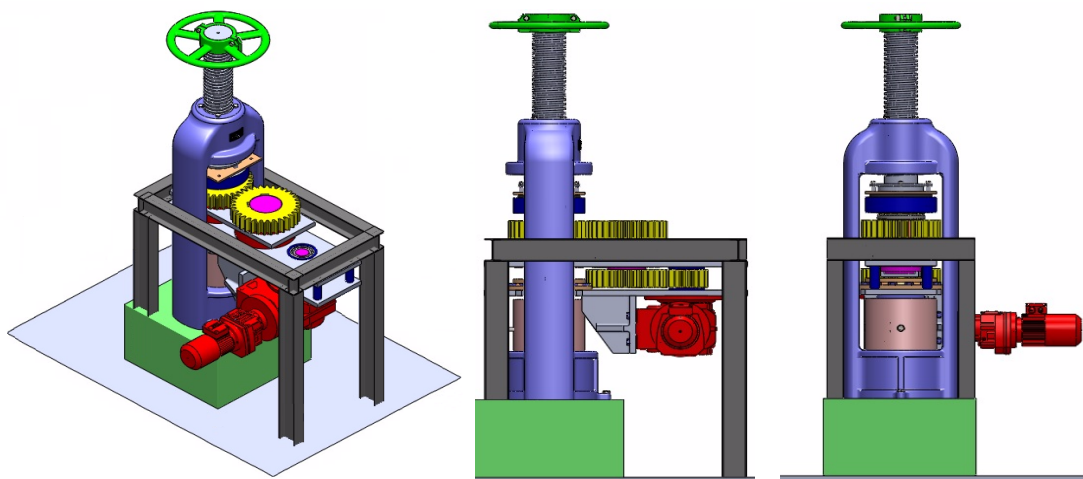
Vistas da montagem do equipamento de ensaio HPT / máquina de ensaio de tração.
